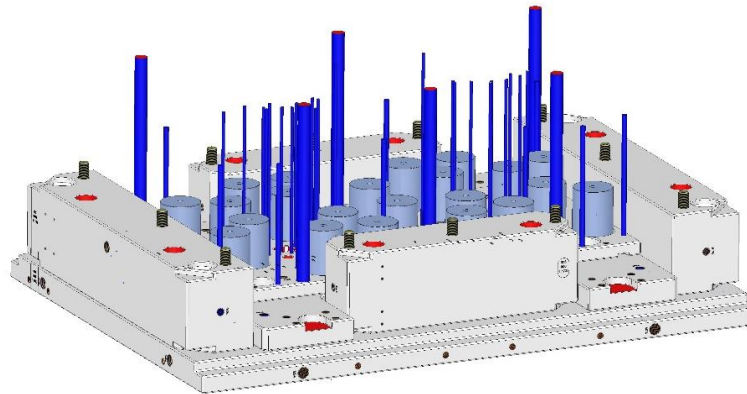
Vista isométrica e frontal da extração do molde e seus componentes, extratores, calços, chapas extratoras, pernos de retorno, fixações, e anel de centragem da extração.
